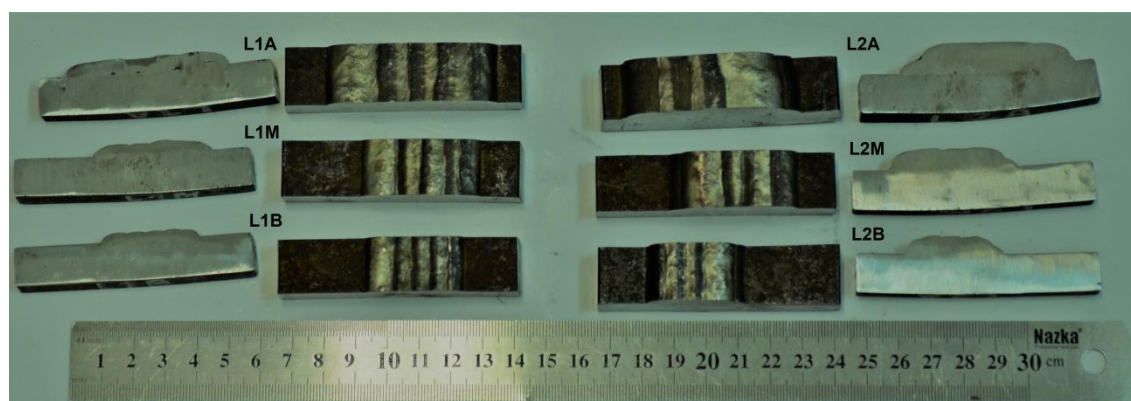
Probetas de soldaduras LDSS, transversales y superficiales.
